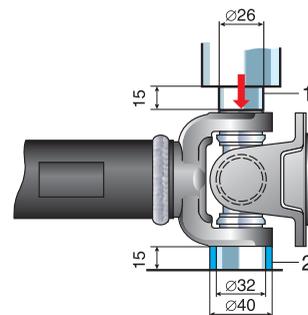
Выпрессовка подшипников карданного шарнира: 1, 2 — оправки
